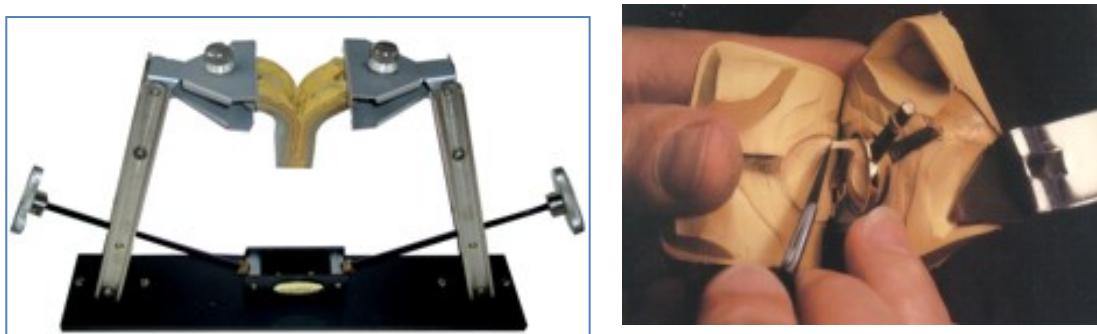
Приспособление для разжатия резиновой пресс-формы
